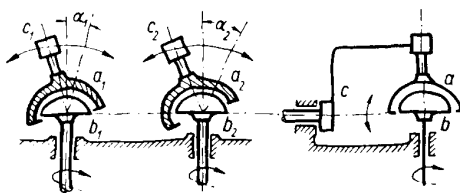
Aufgabenskizze — Arbeitsweise einer Schleif- und Poliermaschine für kugelige Flächen.
